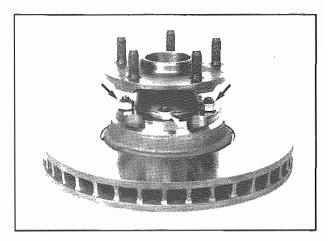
Viti fissaggio campana disco al mozzo Disc housing to hub screws
